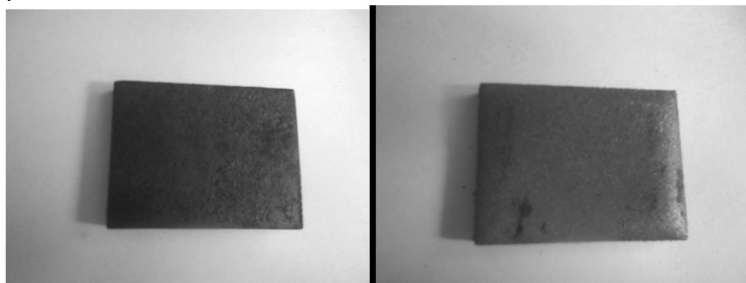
Общий вид образцов до испытаний на изнашивание:
